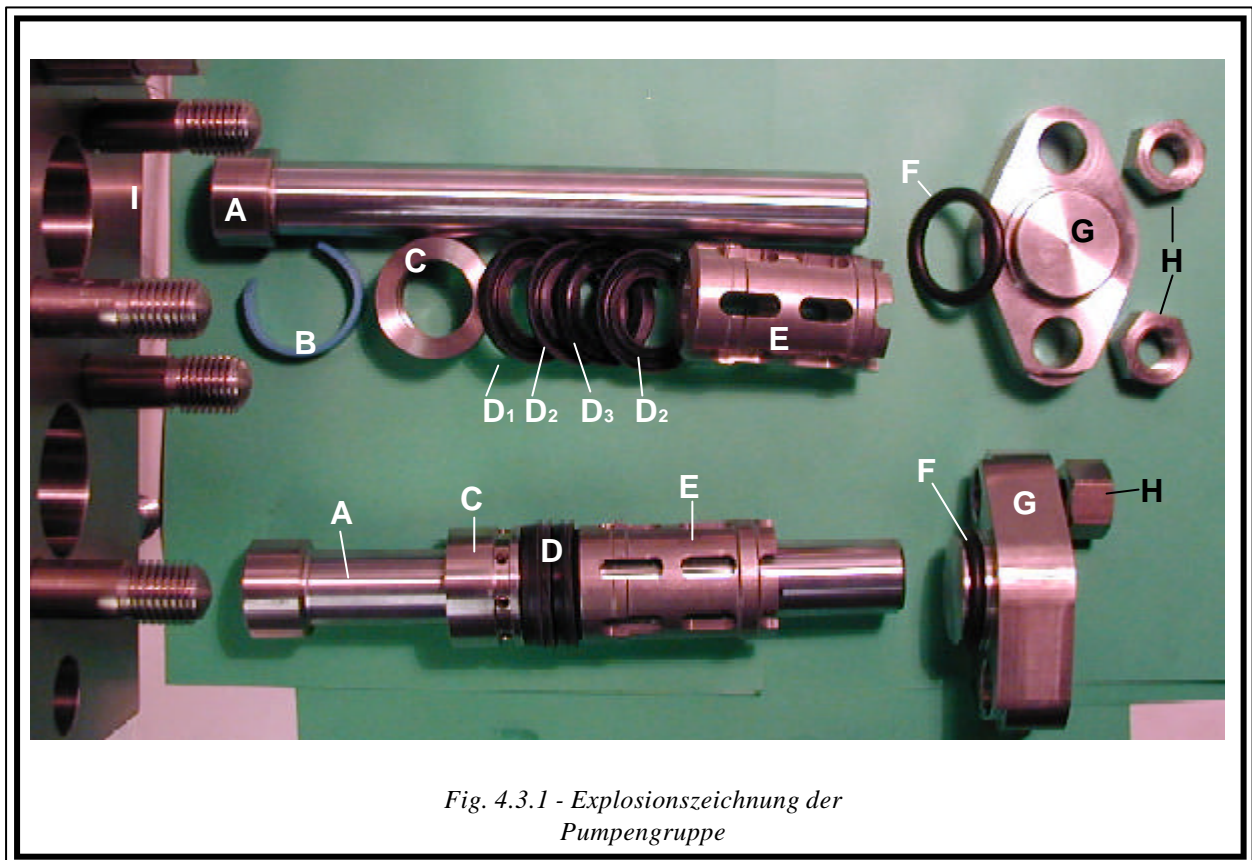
Explosionszeichnung der Pumpengruppe
